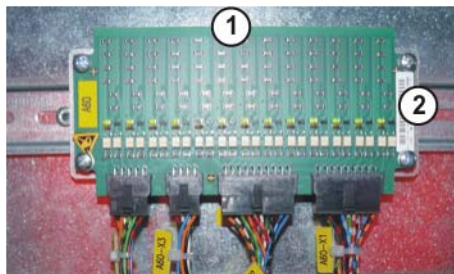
Desbloquear la tarjeta del optoacoplador
